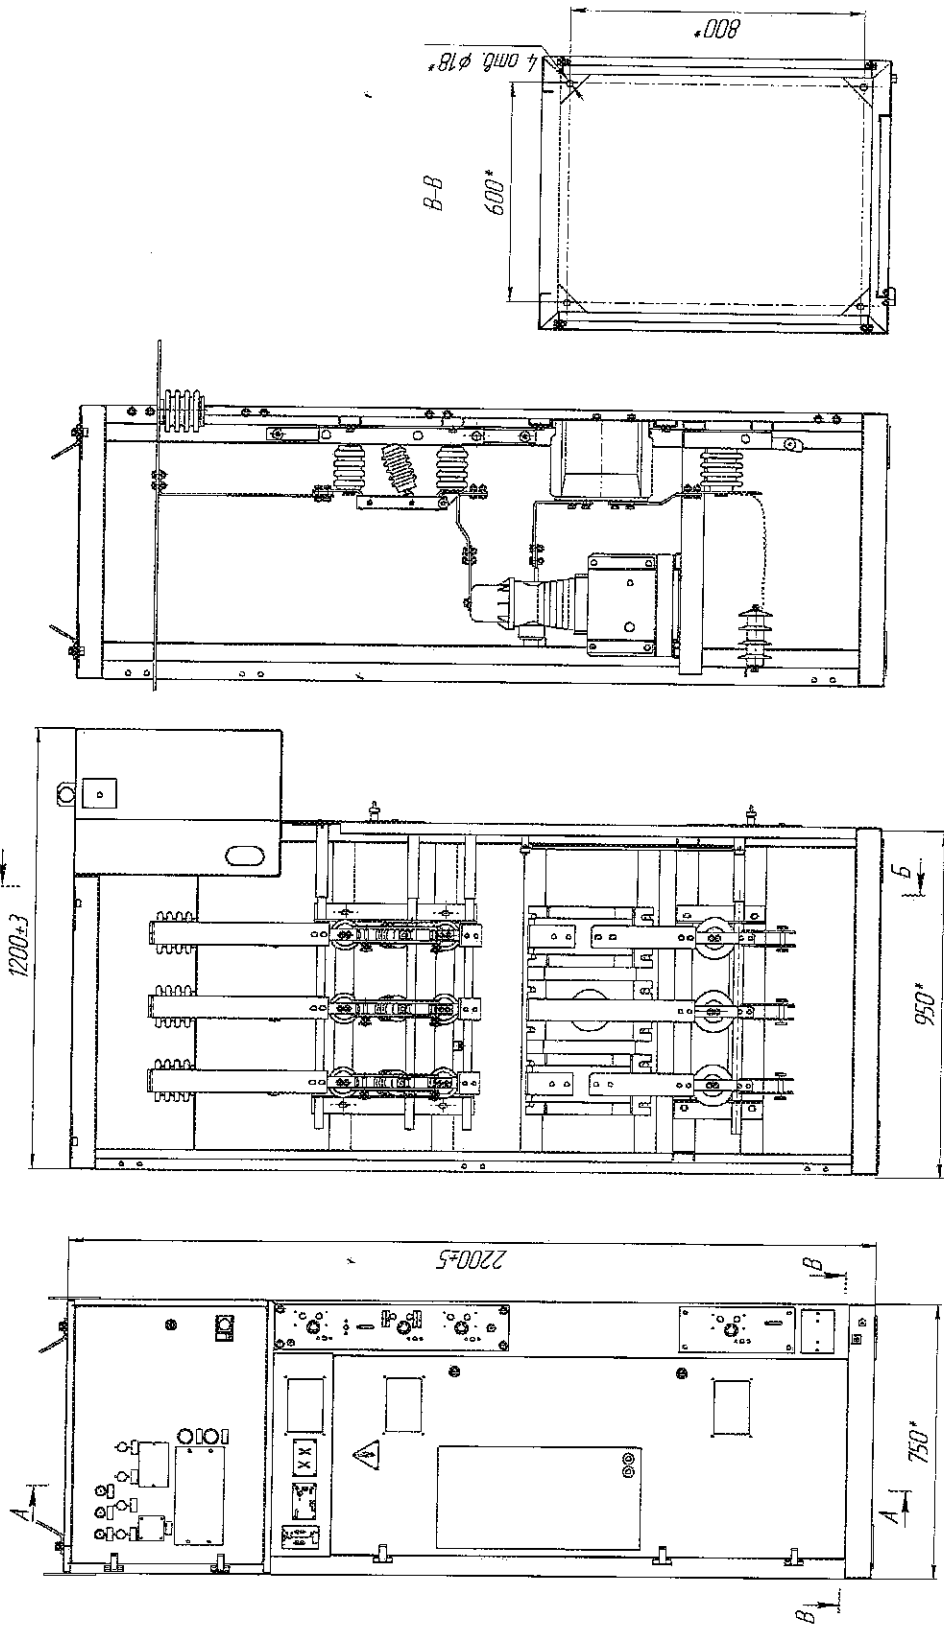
Габаритные, установочные, присоединительные размеры КСО-202ВМ с выключателем СМ/ТЕЛ
